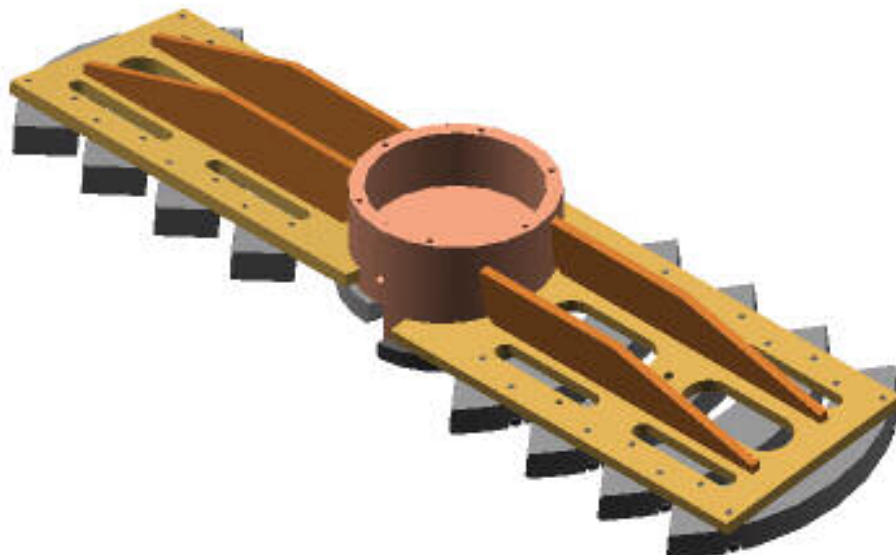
Profilhalterung mit Gleitprofilen (ursprüngliche Ausführung)⁵
